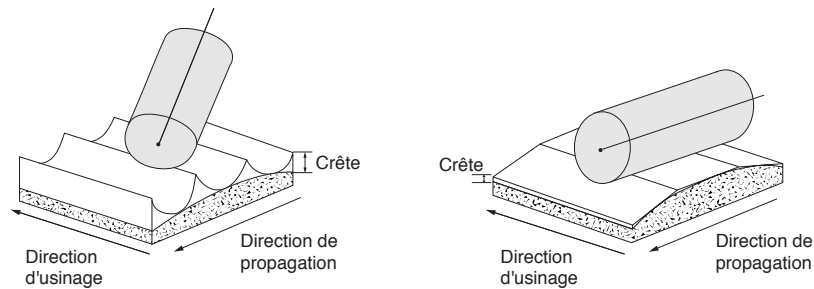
Usinage en bout et sur le flanc [Takeuchi et al., 1995]
